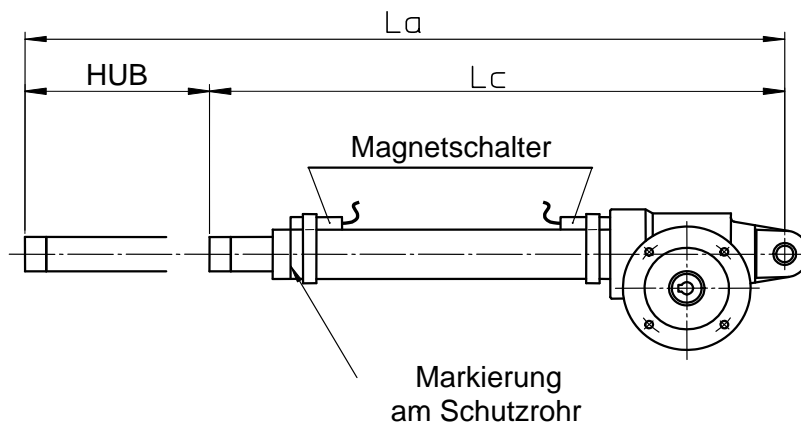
Linearantrieb mit magnetischen Endschalter
